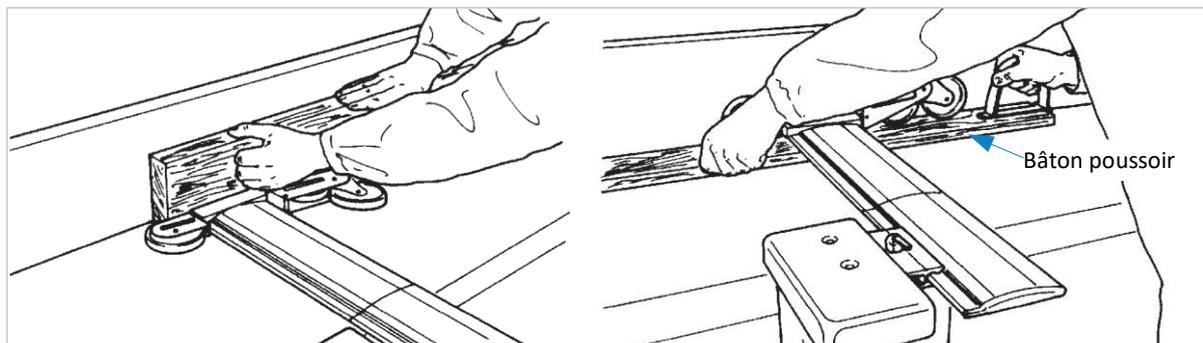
rabotage de pièces de petite section et rabotage du côté de la pièce
